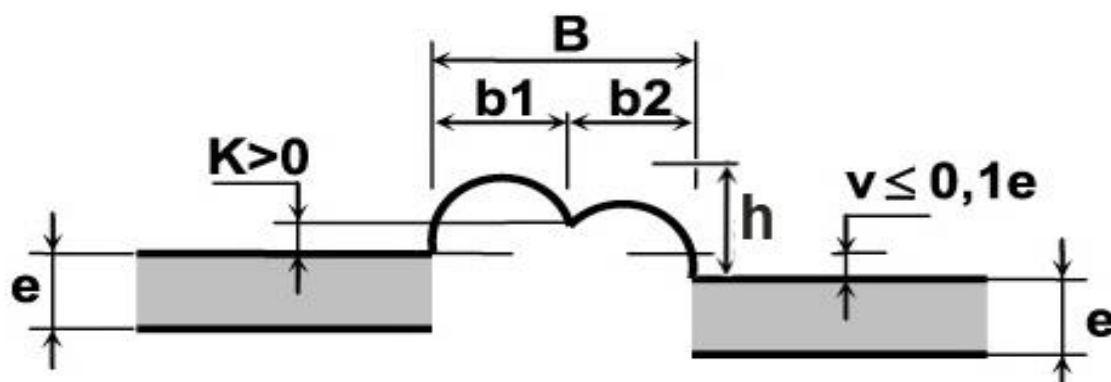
Основні розміри валиків грату стикового зварного з'єднання поліетиленових труб
